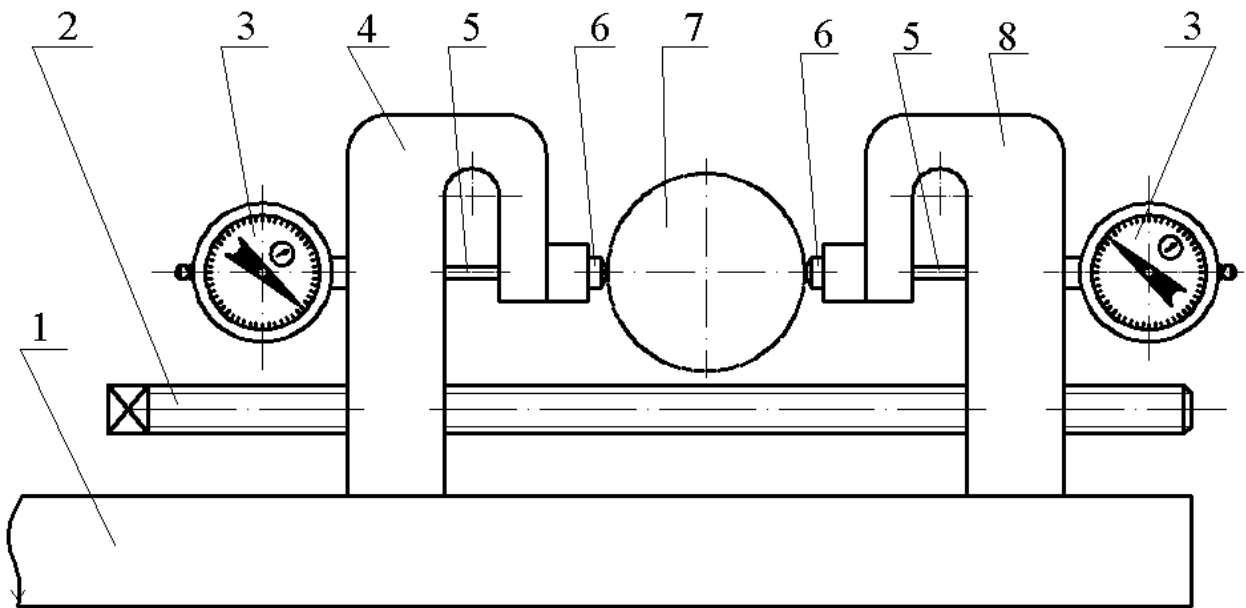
Пристосування для вигладжування поверхонь обертання: 1 – основа, 2 – гвинт ходовий, 3 – індикатор годинникового типу, 4 – стійка ліва, 5 – шток індикатора, 6 – вигладжувач, 7 – оброблювана заготовка, 8 – стійка права.
